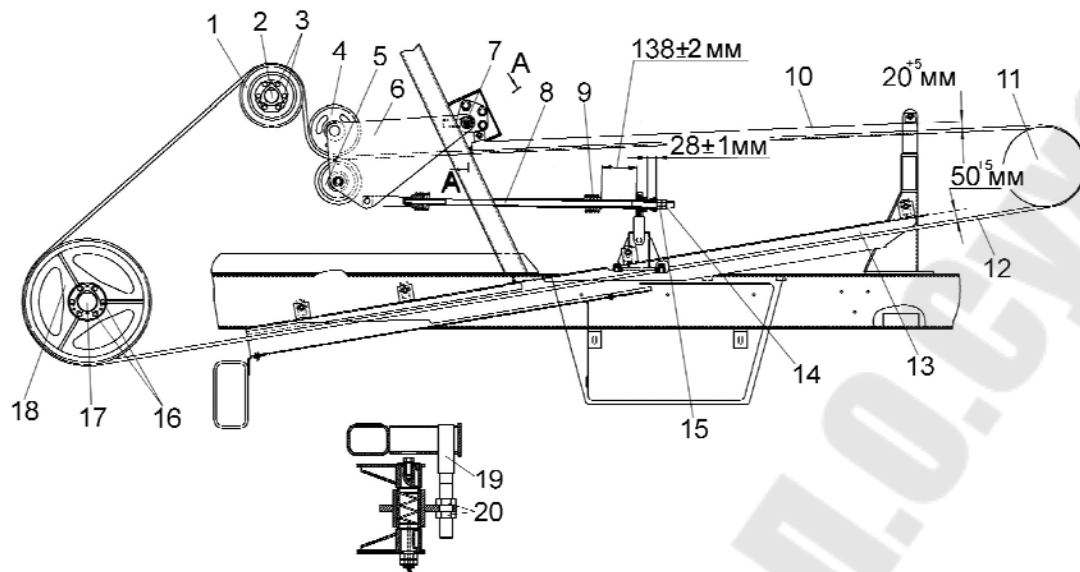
Привод измельчающего барабана: 1, 11, 18 – шкивы; 2, 17 – валы; 3, 16 – болты; 4, 5 – ролики; 6 – рычаг; 7, 15, 20 – гайки; 8 – винт; 9 – пружина; 10, 13 – щитки; 12 – ремень; 14 – контргайка; 19 – шпилька
